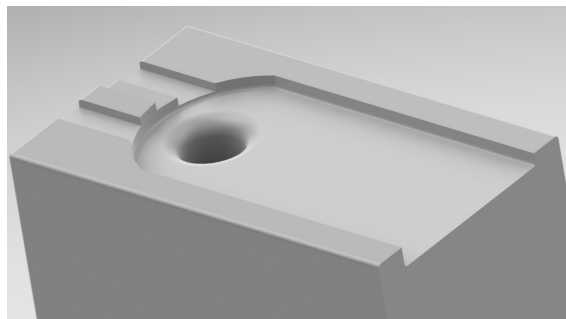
Насадка для сварки нахлесточного соединения
